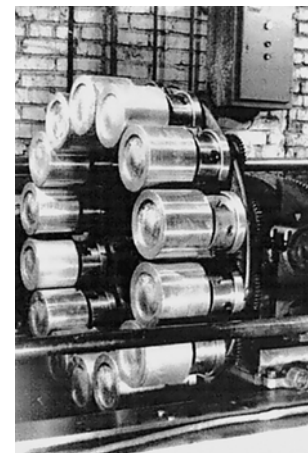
14-позиционный манипулятор для сварки и упрочнения поршней
